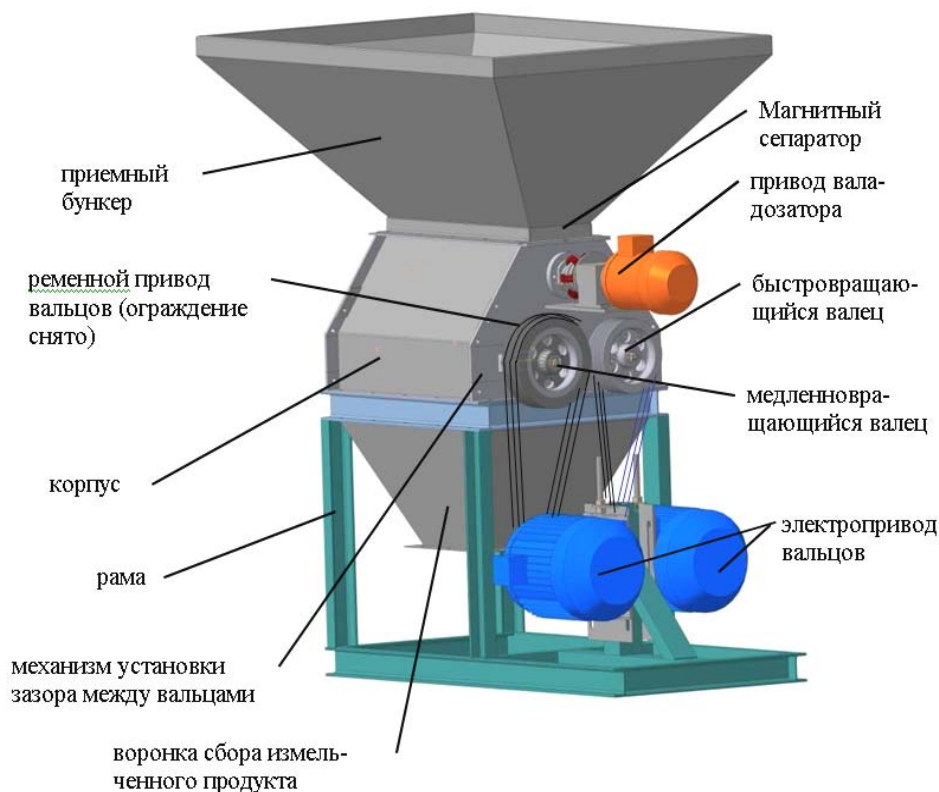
Схема конструкции экспериментального образца вальцовой дробилки
